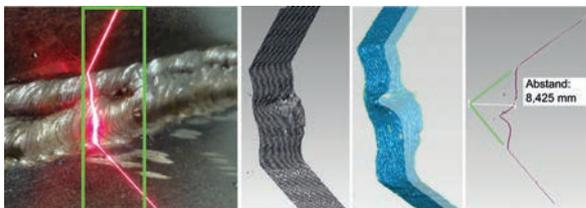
Messung einer Schweißnaht an Luft; von links nach rechts: Schweißnaht mit projizierter Laserlinie, Punktwolke, Schnitt durch vermaschte Punktwolke und Profil mit Maßangabe.
